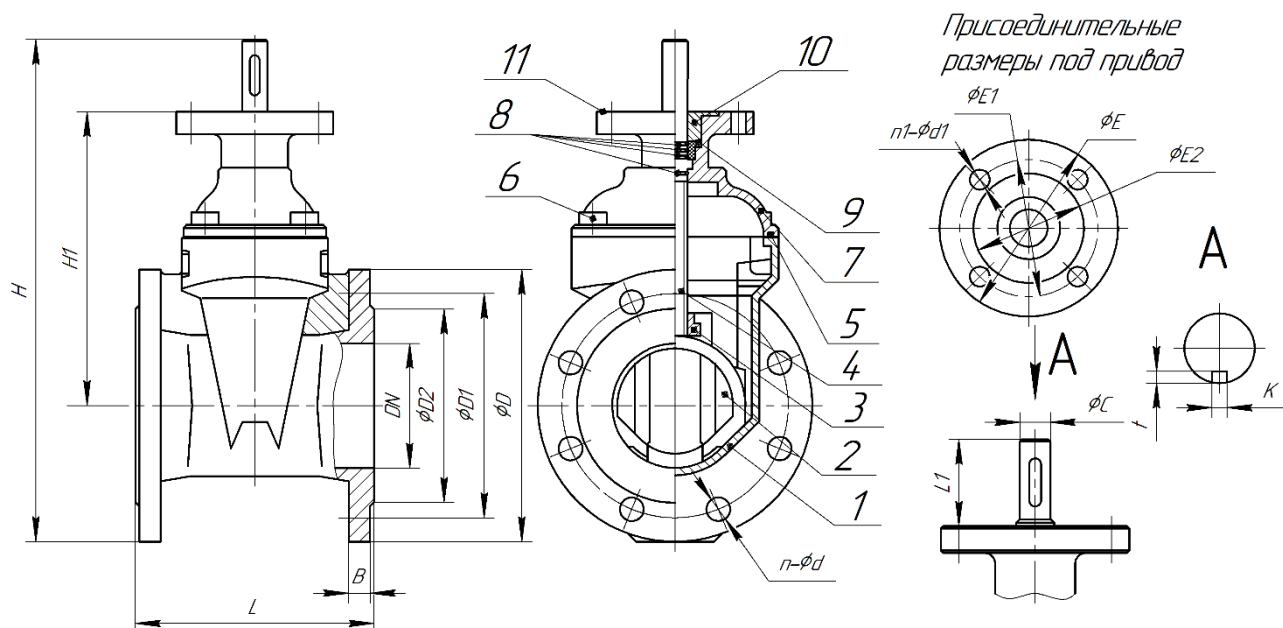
Задвижка 47GVA.Z без исполнительного механизма DN350-800
